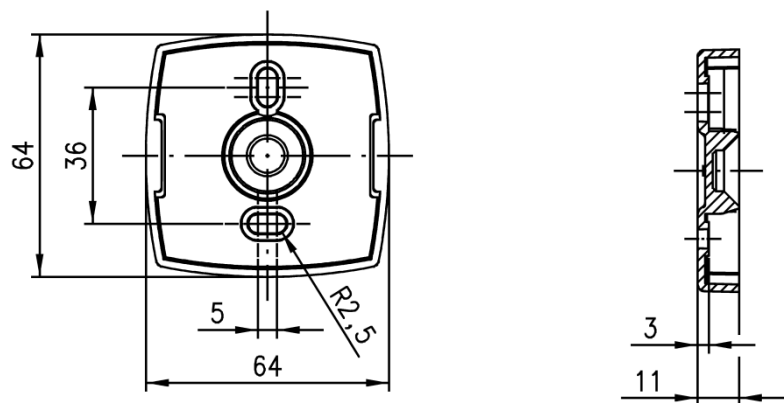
Draufsicht und Querschnitt von der Adapterplatte
